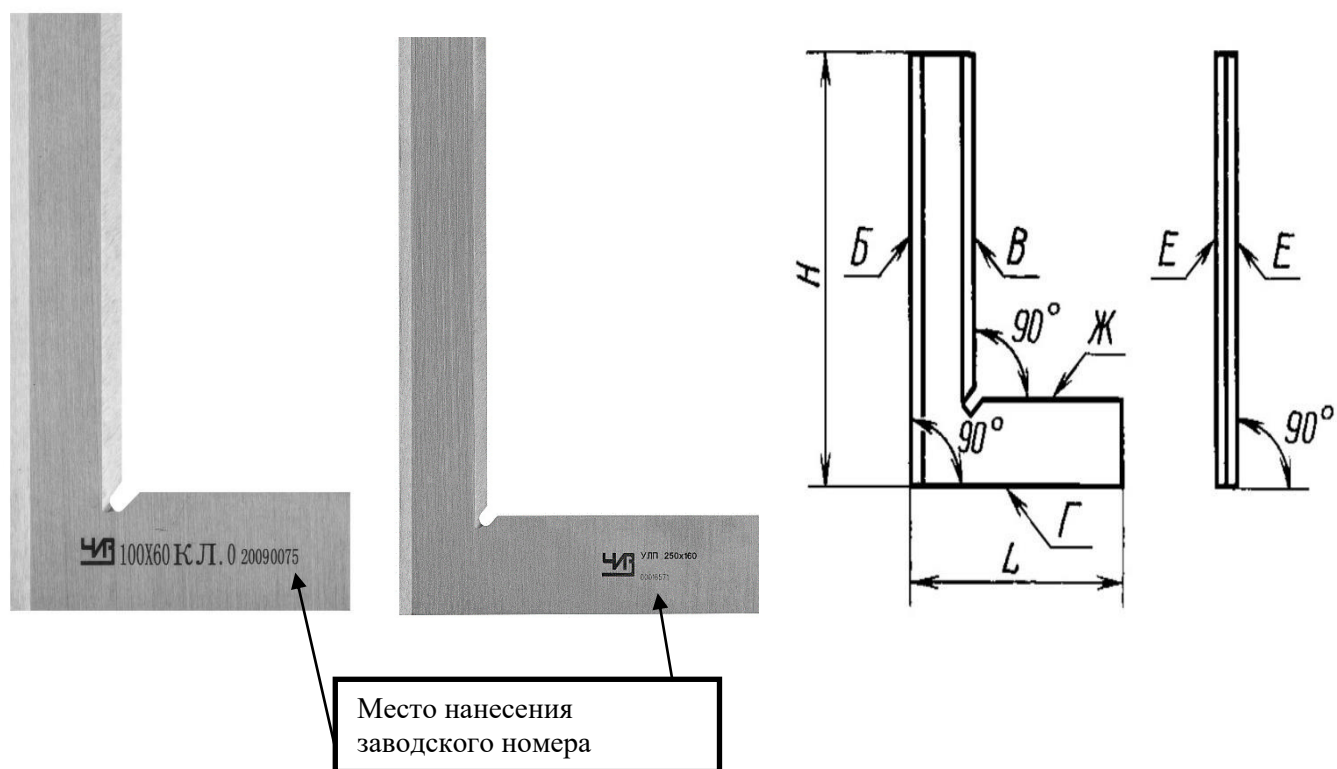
Общий вид угольников типа УЛП с местом нанесения заводского номера и обозначение условных размеров и поверхностей
